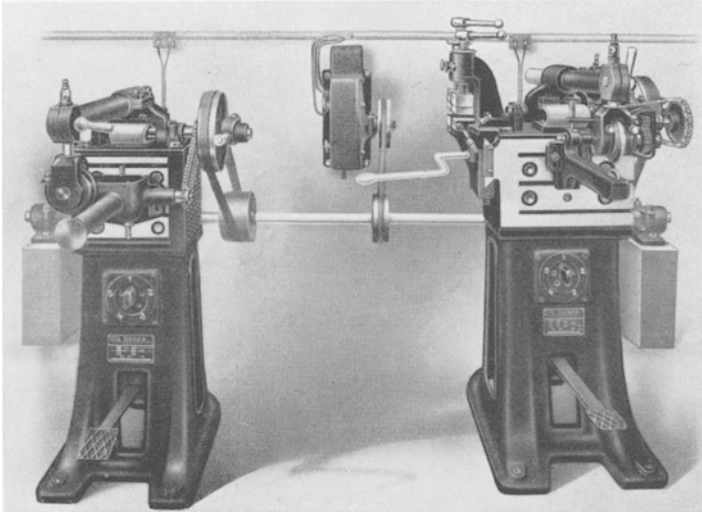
Längs- und Quernahtschweißmaschinenpaar mit Transmissionsantrieb und Stromunterbrecher.
